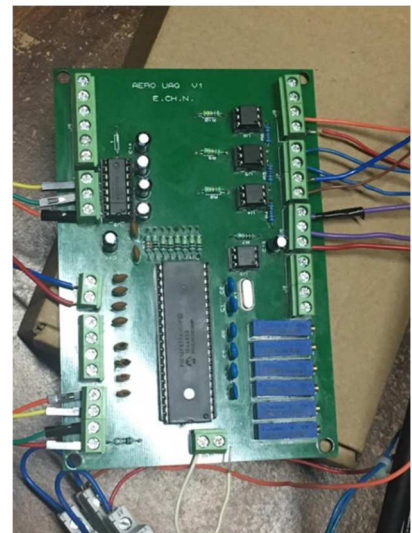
Diseño de la PCB para el circuito eléctrico de control.
